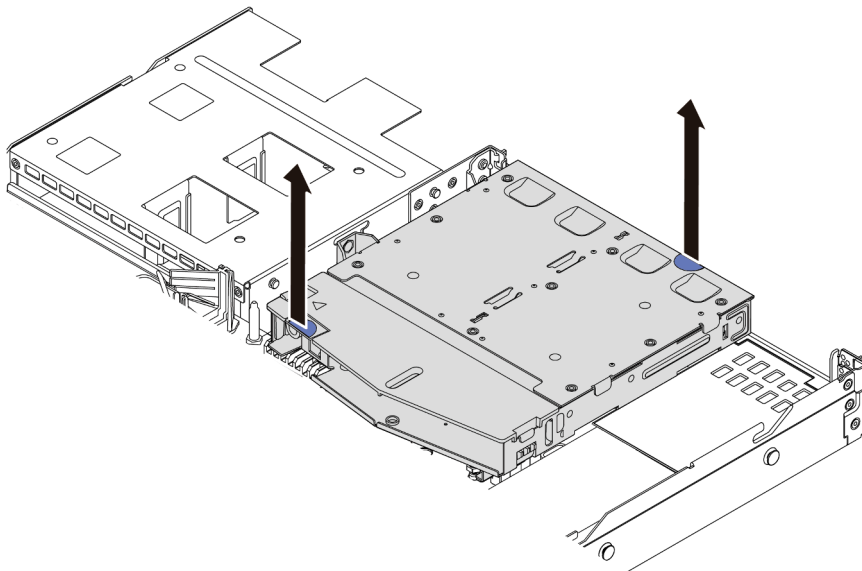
Entfernen der hinteren Hot-Swap-Laufwerkhalterung
